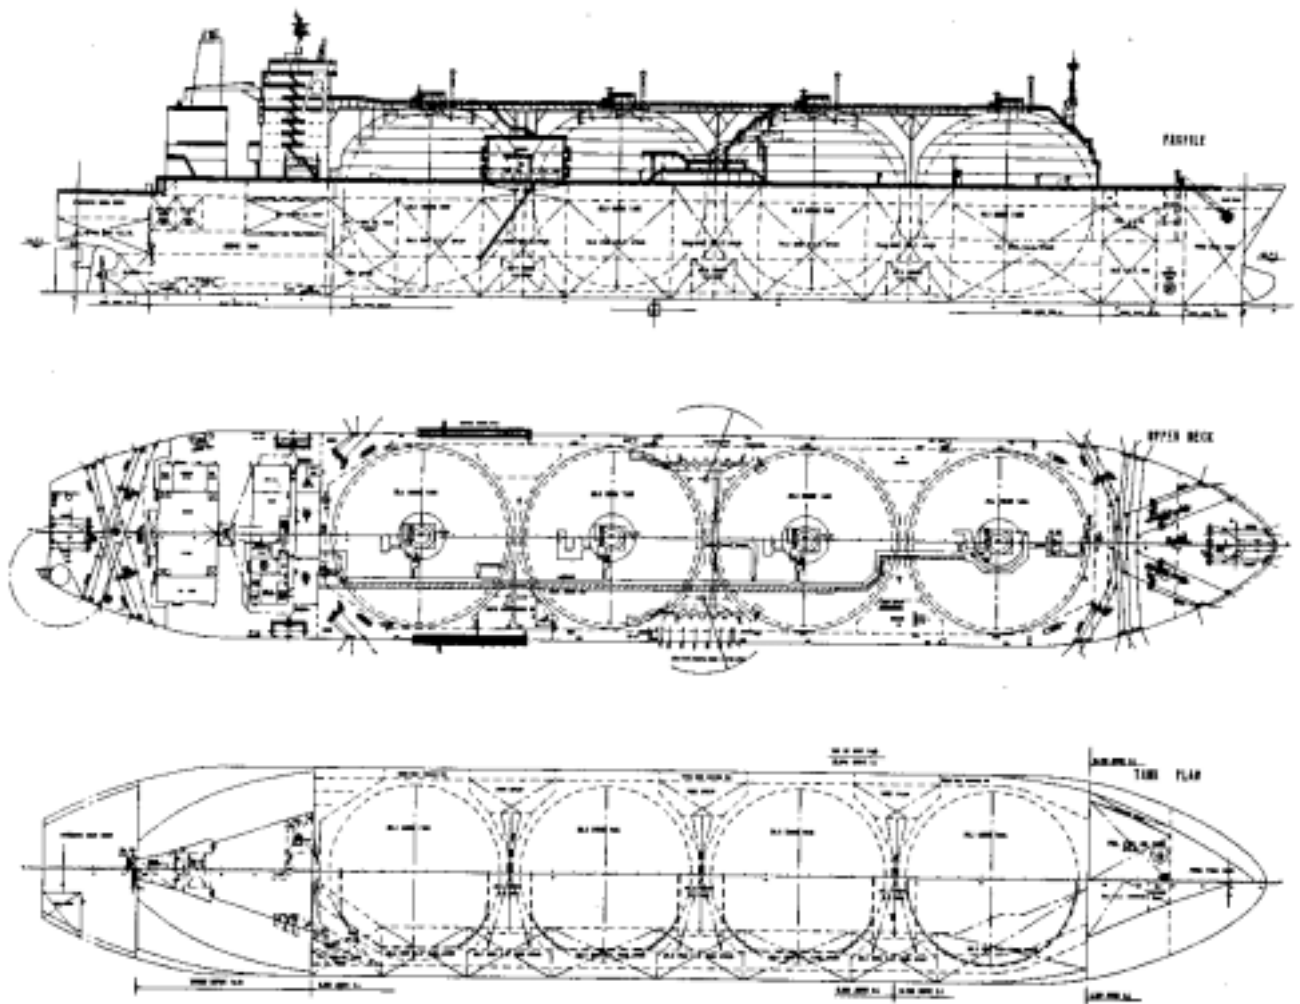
Схема общего расположения газовоза «LNG Rivers» со сферическими грузовыми танками
